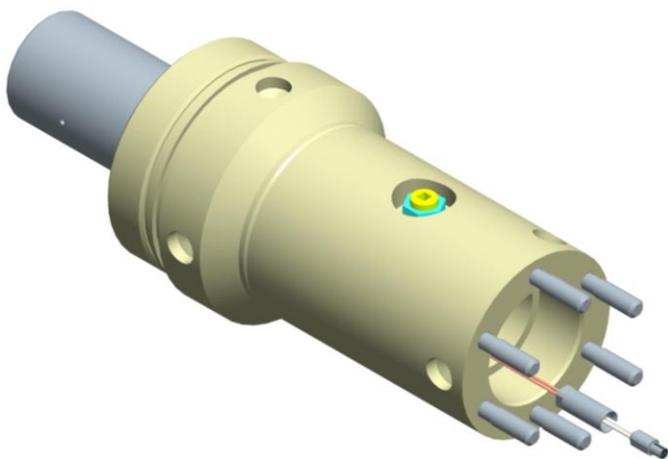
Внешний вид БП-103М3-400-В2-Т2М-33
